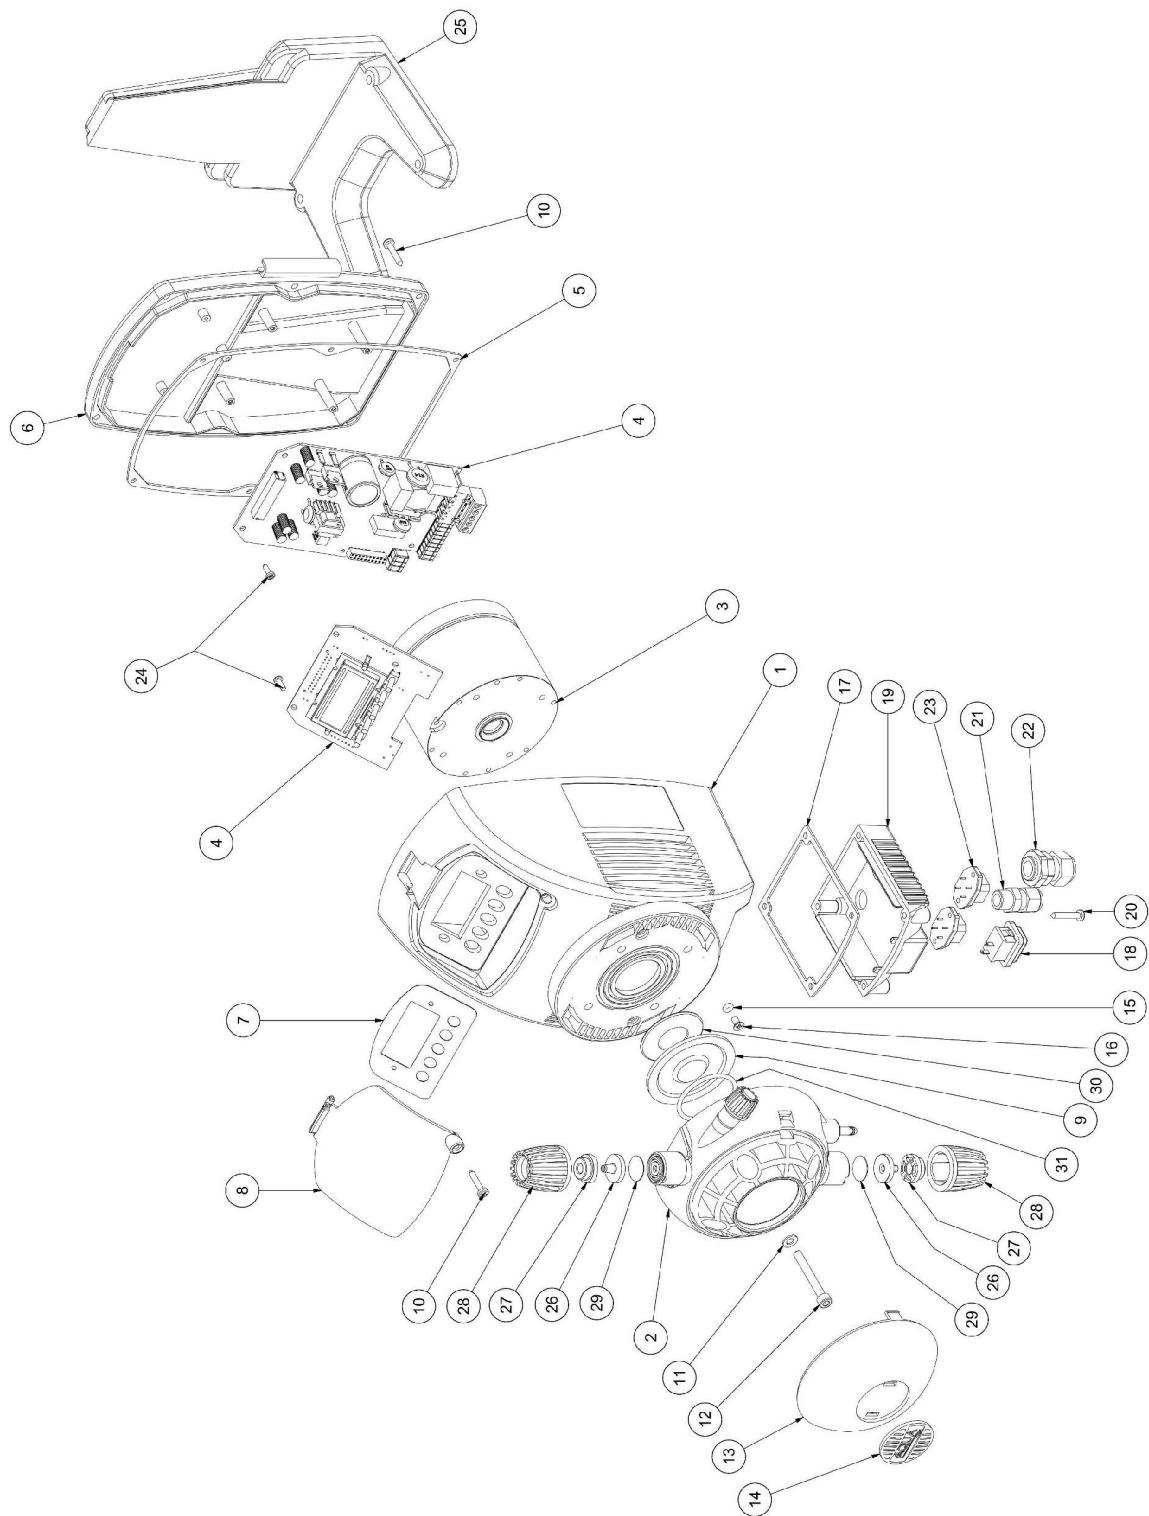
SERIE HC 997 - Espreso / Opis / Explosive / Dibujo/ Explosionszeichnung / ртеж
